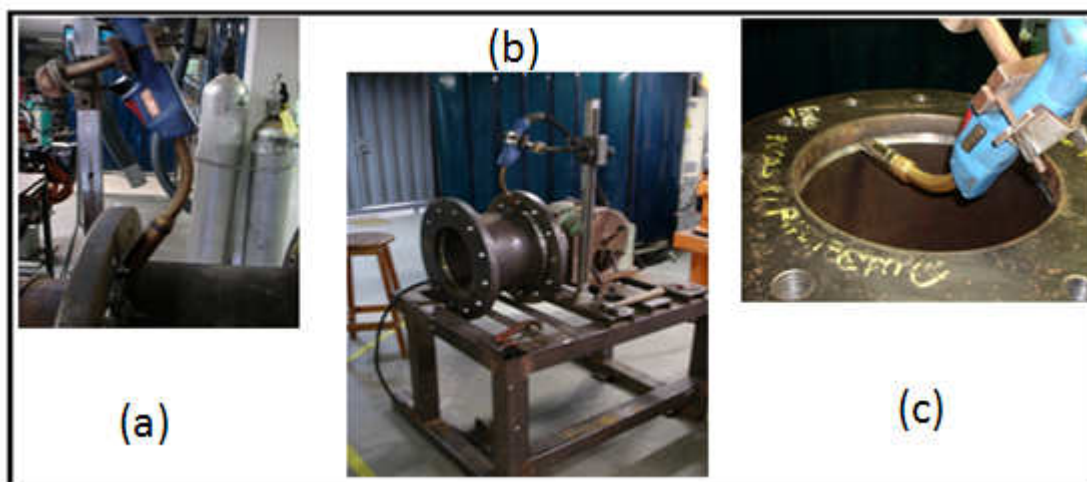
Esquema da solda dos flanges na tubulação. (a) - Solda externa do anel de aço no corpo central; (b) - Dispositivo de solda utilizado; (c) - Solda interna do anel de aço no corpo central.
